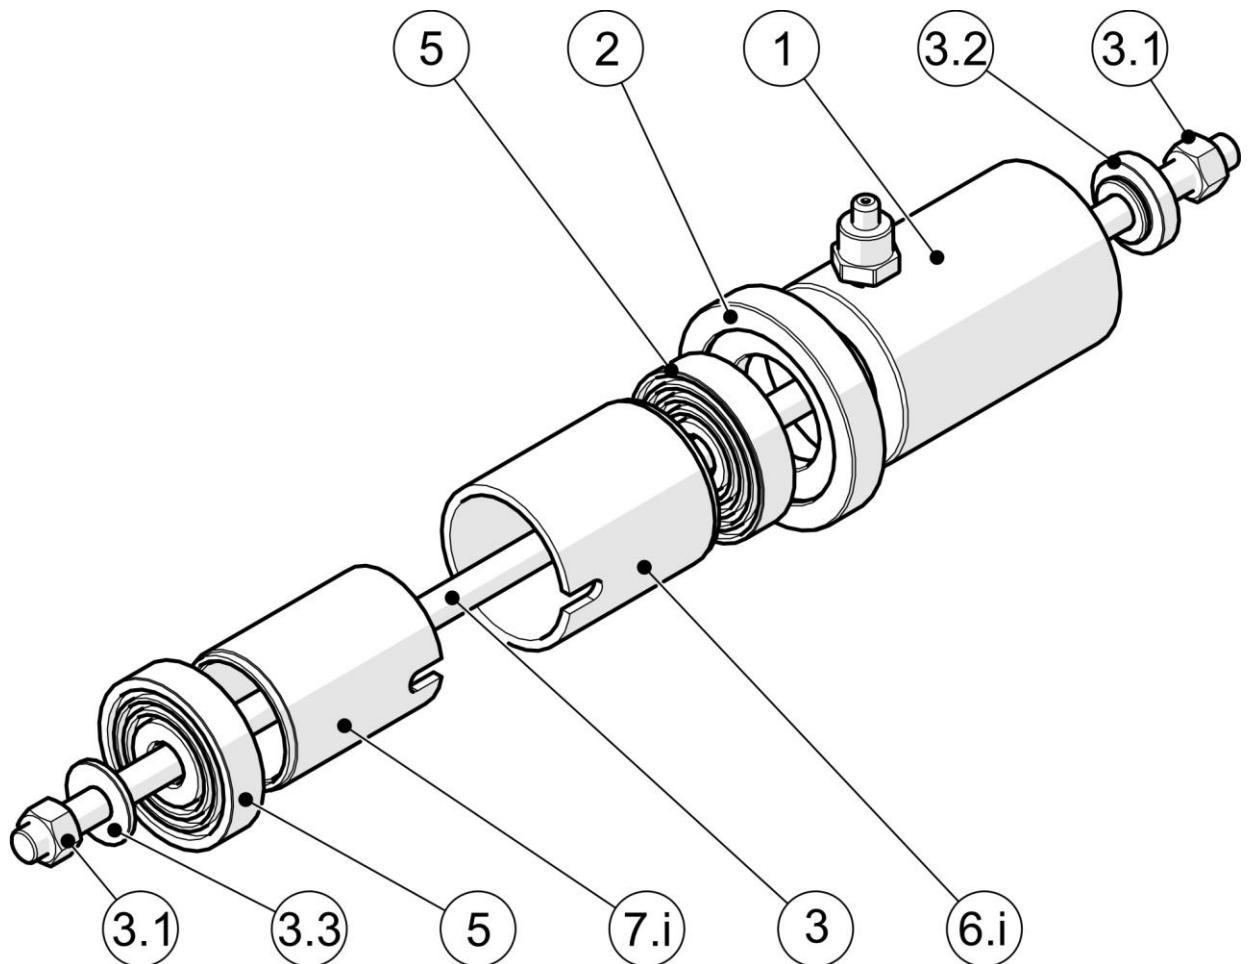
Основные элементы выпрессовщика на примере шпильки M16
